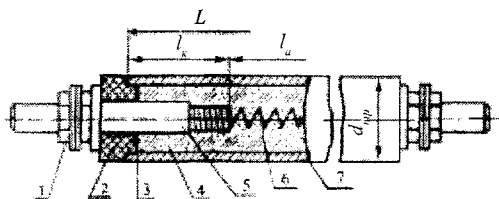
Типовая конструкция трубчатого нагревателя: 1 – контактный узел; 2 – изолятор; 3 – герметик; 4 – наполнитель; 5 – контактный стержень; 6 – нагревательная спираль; 7 – металлическая оболочка; L, l_a, l_k – длина габаритная, активной и контактной части
